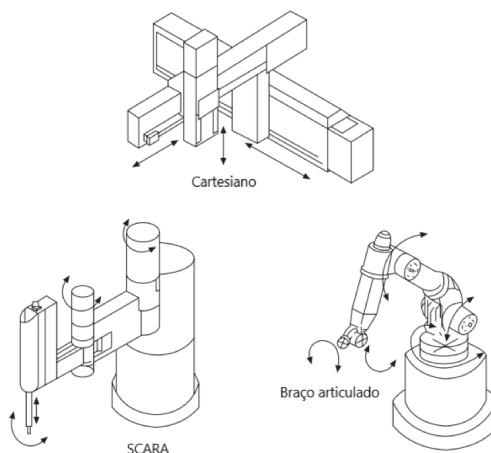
Configurações típicas de *robots* de soldadura (Adaptado de: Norrish, 2006)
